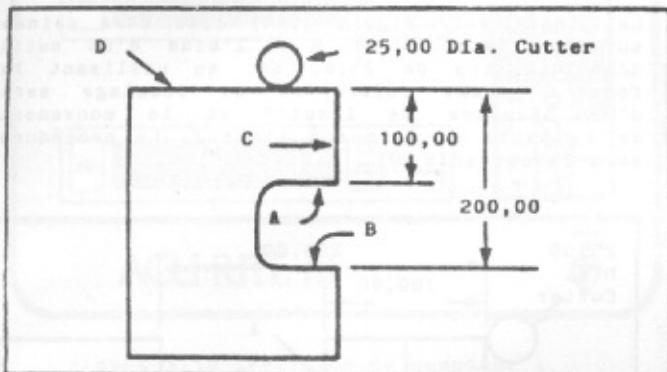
Pièce pour procédure B - compensation de l'outil
